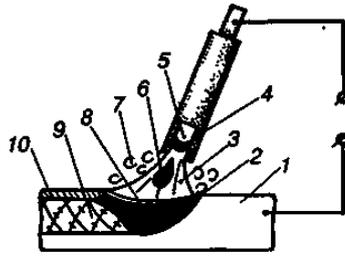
Схема процесса ручной дуговой сварки покрытыми электродами
